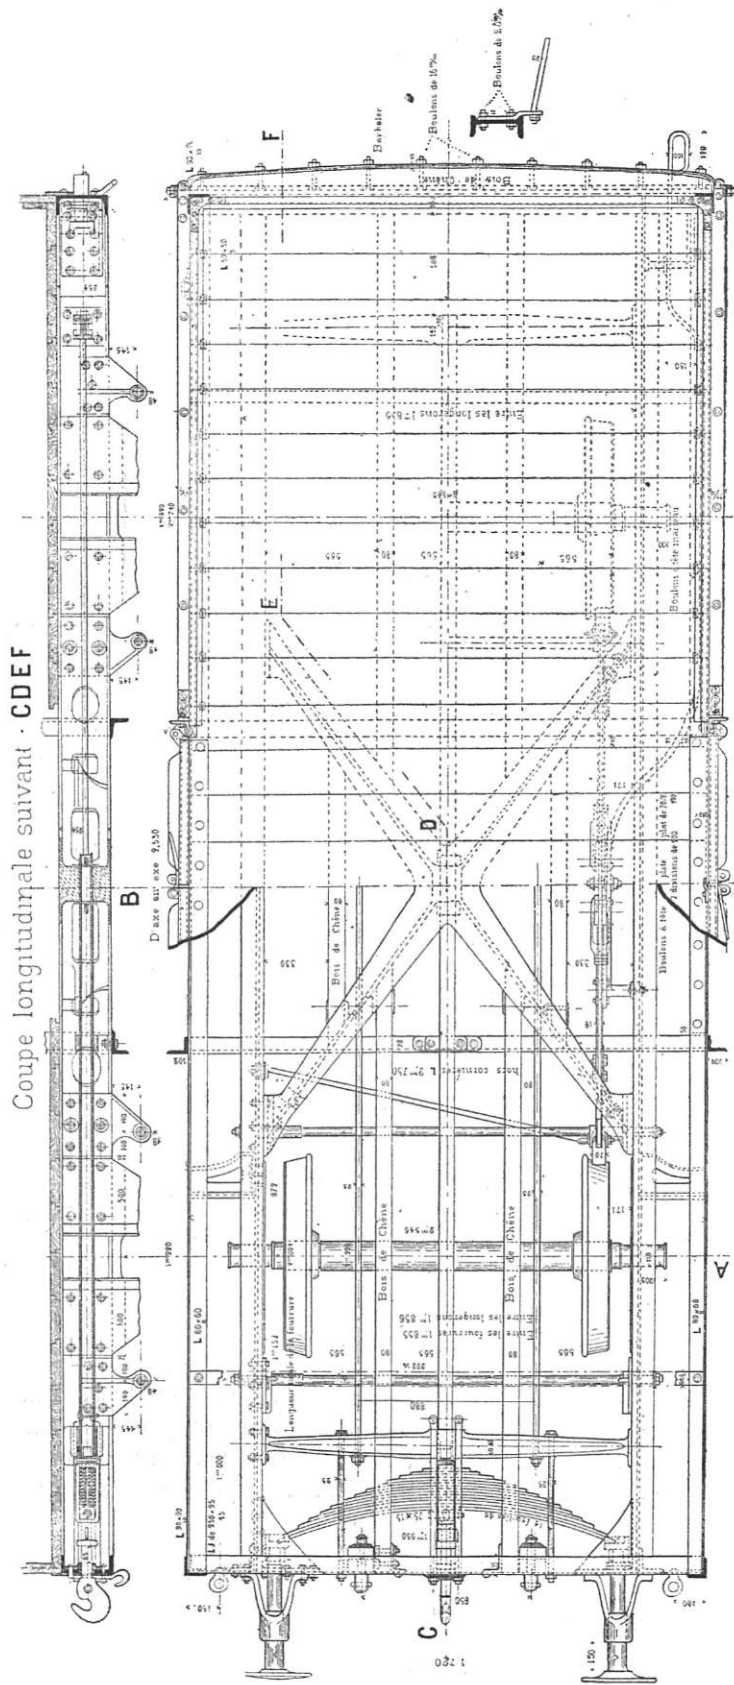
et 3 — Vue en plan et coupe longitudinale.
